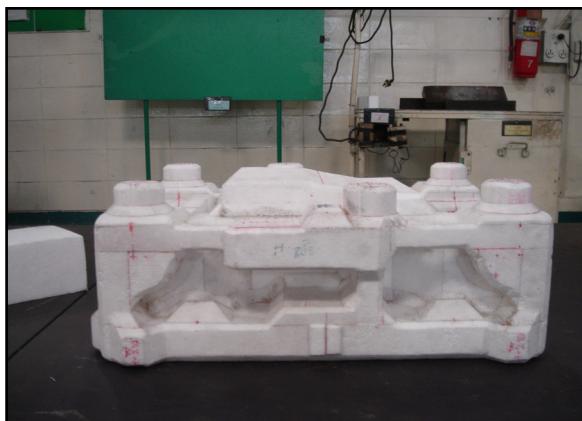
ชิ้นงานแบบหล่อแม่พิมพ์(FULL MOLD CASTING)
